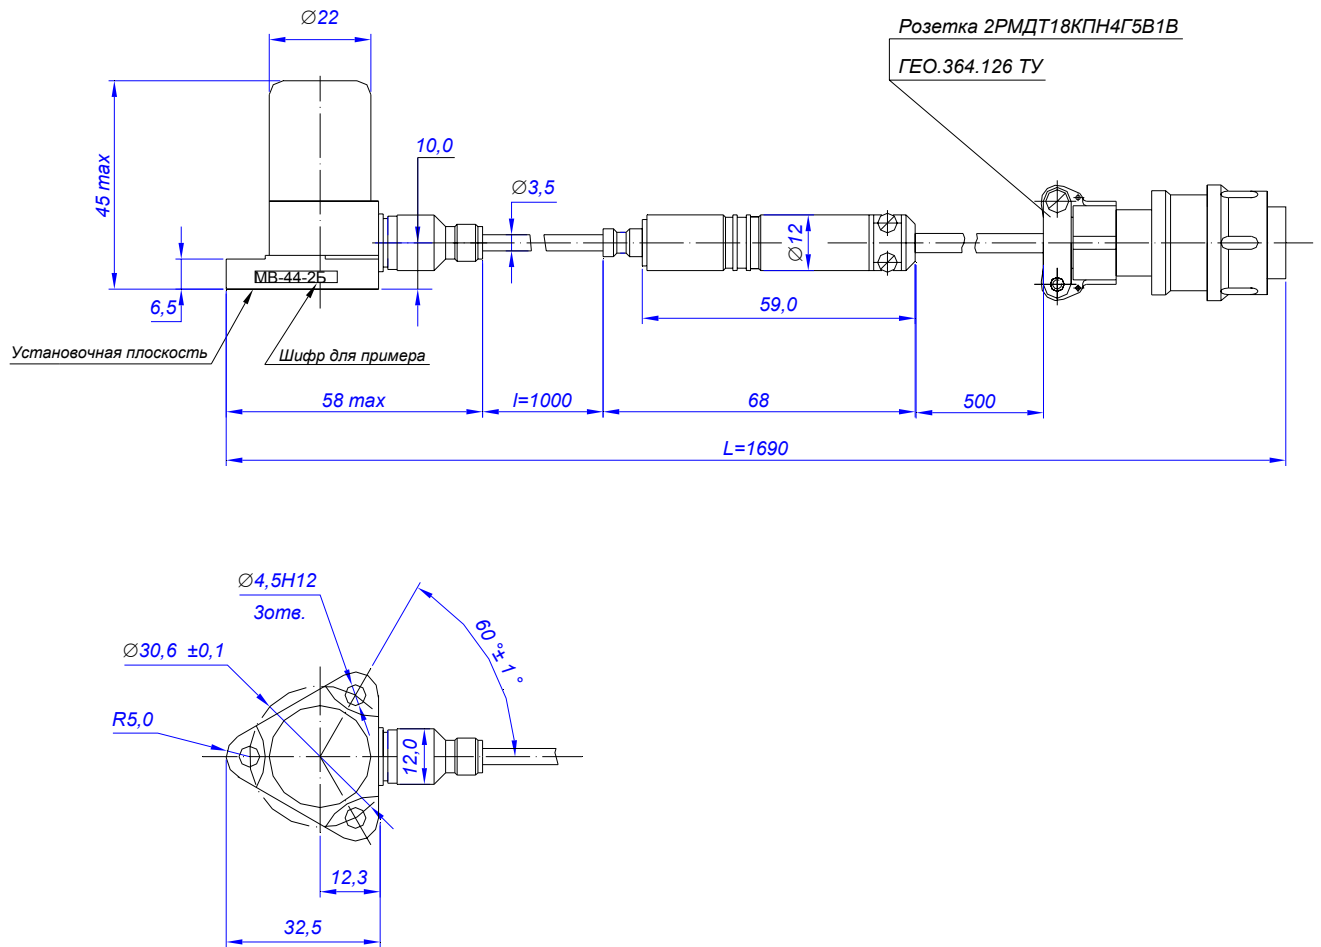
Габаритно-установочные размеры датчика вибрации MB-44-2B/1,0/0,5
